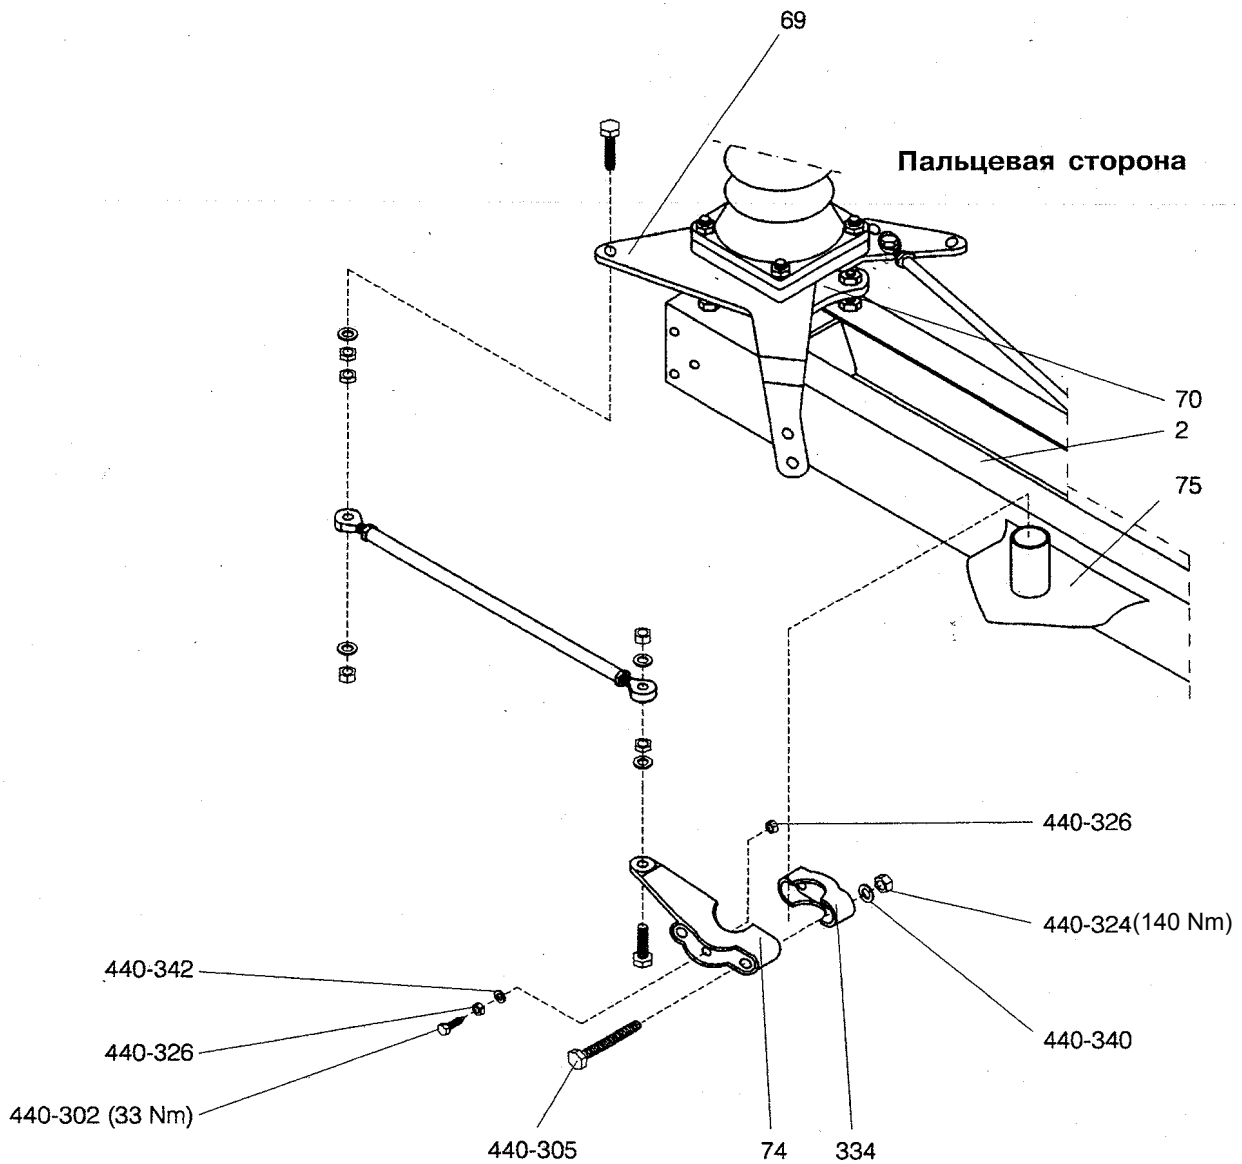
Установка приводного механизма разъединителя, непосредственно на основании полюса. Установка приводного рычага (74) при расположении приводного механизма разъединителя на стороне противоположной открыванию
